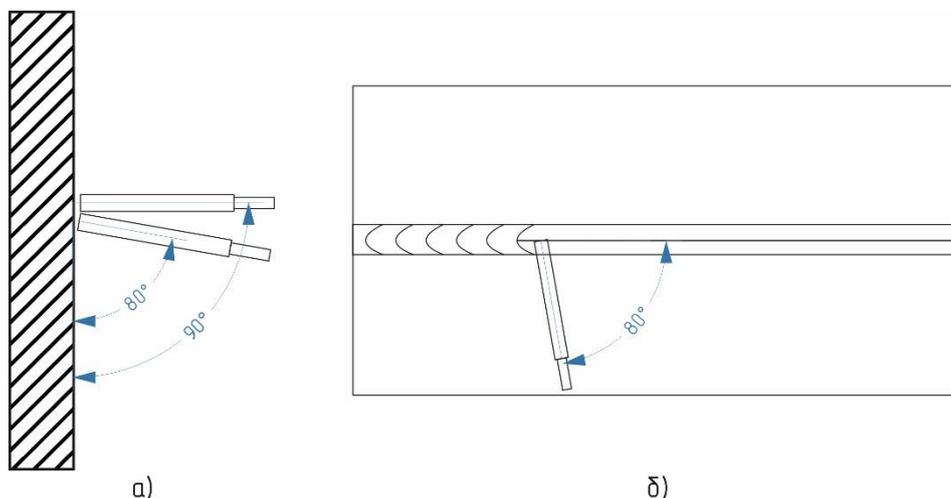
Положения электрода при сварке в горизонтальном положении: а) – относительно вертикальной плоскости детали; б) – относительно направления сварки
